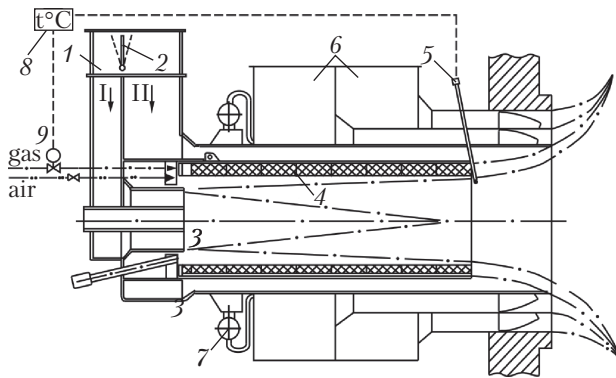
Схема конструкції пальника з ТХП для котла ТПП-210А: 1 – короб пилоподачі; 2 – поворотний шибер; 3 – запальний пристрій; 4 – муфельна камера термообробки пилу; 5 – датчики температури; 6 – короб подачі вторинного повітря; 7 – існуючий газовий колектор; 8 – контроль температури; 9 – регулятор подачі газу на процес ТХП
